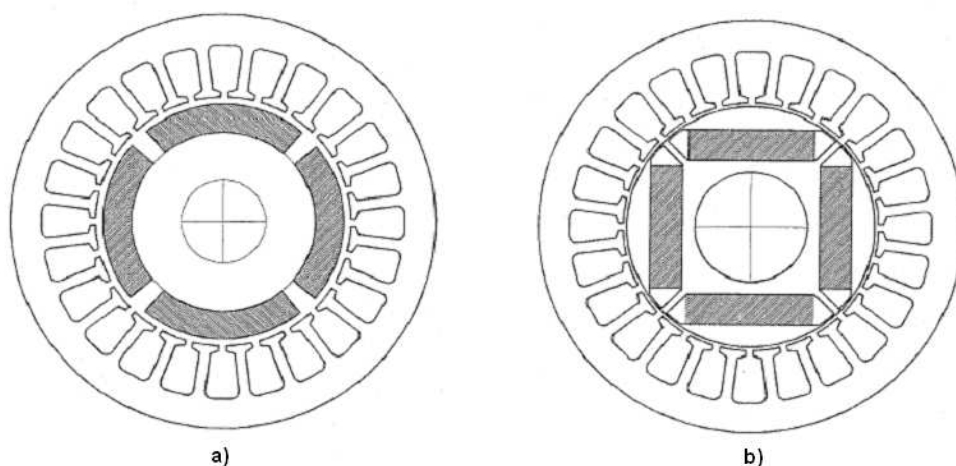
Motory s a) radiálním tokem b) axiálním tokem
